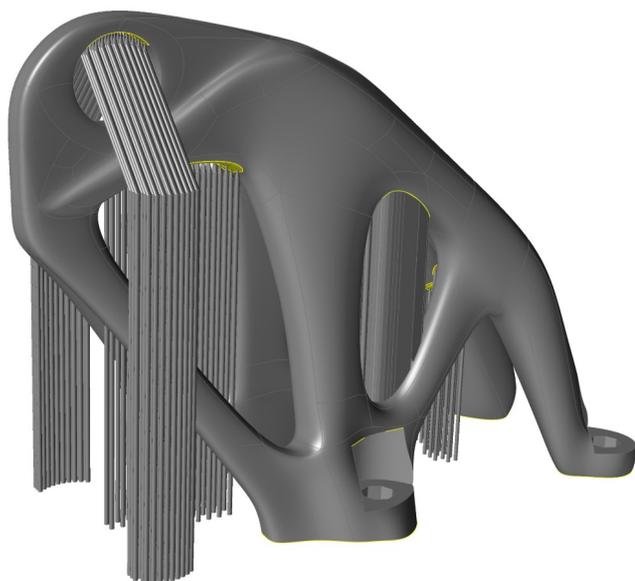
Pieza en aluminio preparada para imprimir en 3D generada mediante Altair Inspire
